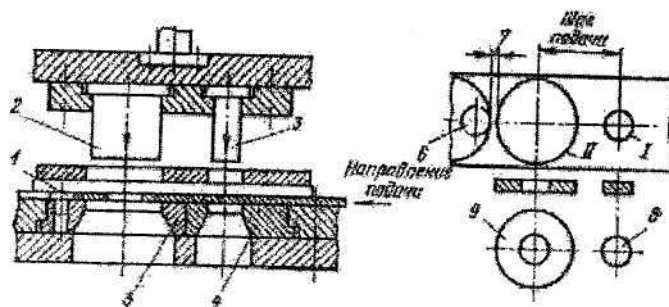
Схема штампа последовательного действия для пробивки и • вырубki: 1 - упор; 2 - пуансон вырубki; 3 - пуансон пробивki; 4 - матрица пробивki; 5 - матрица вырубki; 6 - упор; 7 - перемычка; 8 - отход; 9 - изделие
